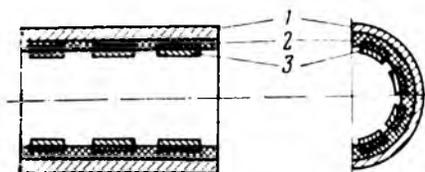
Схема футеровки коробдрочного барабана КБ-6
